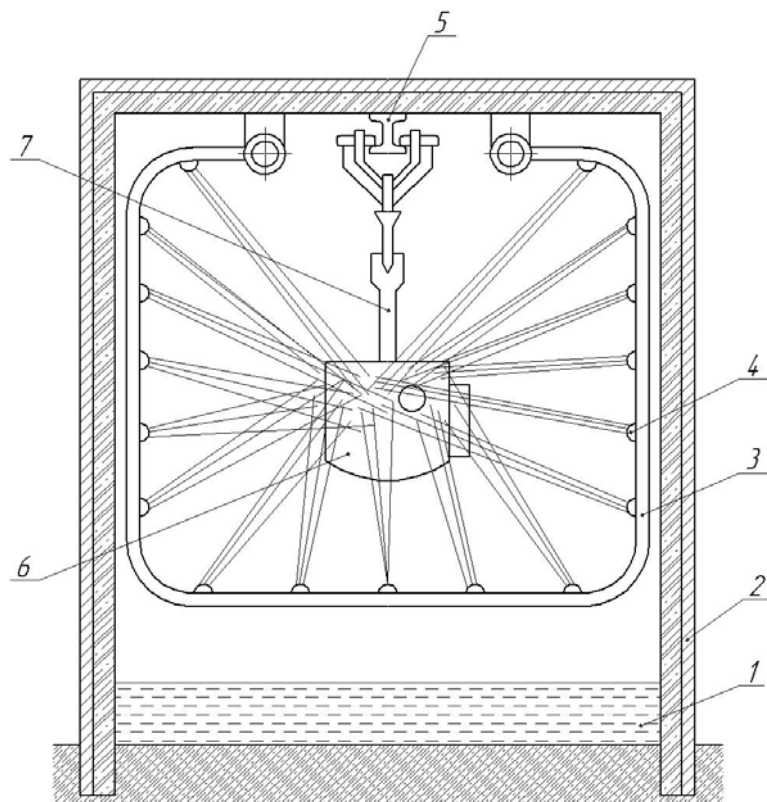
Камера прохідного типу для струменевого миття деталей з підвісним конвеєром:
